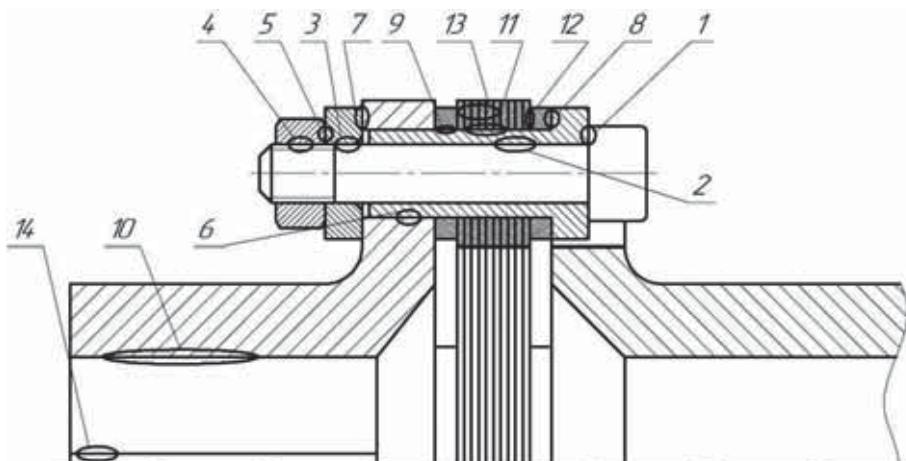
Поверхні пружної муфти з металевими елементами, що піддаються фретинг-корозії.
